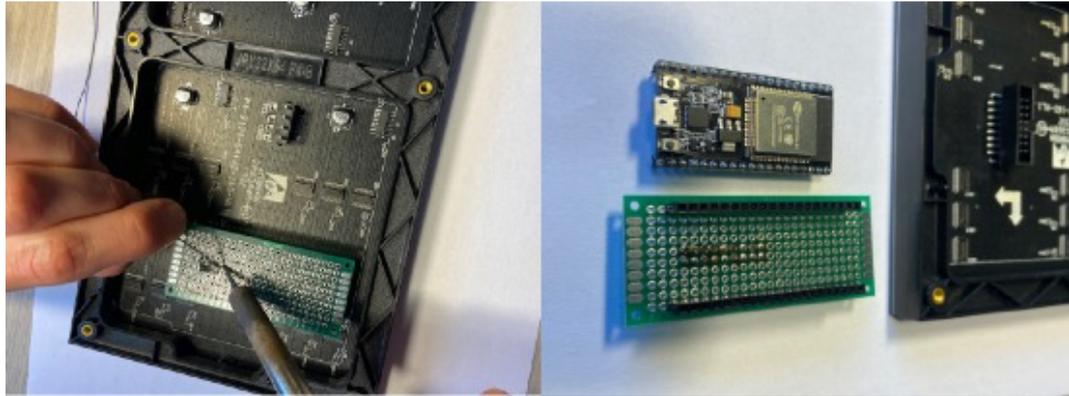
Continuamos el proceso soldando los pines hembra con la placa PCB, según la parte izquierda de la ilustración. Después de haber soldado los 16 pines hembra a la placa, preparamos las otras 2 láminas de 19 pines hembra, el número que corresponde a los pines del microcontrolador esp32.
